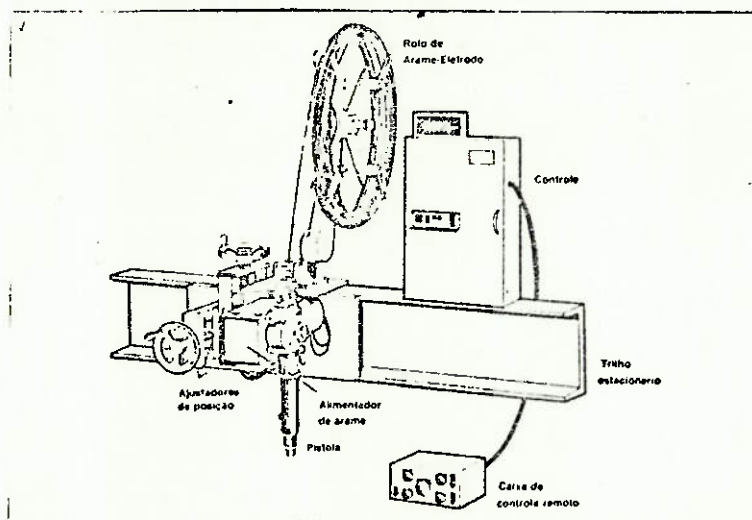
CABEÇOTE PARA SOLDAGEM MIG/MAG AUTOMÁTICA
